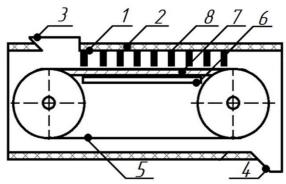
Установка контактного типа для сушки зерна: 1 – кожух; 2 – материал теплоизолирующий; 3 – бункер загрузочный; 4 – окно выгрузное; 5 – рабочий орган; 6 – нагревательный элемент; 7 – пластина; 8 – стержни
